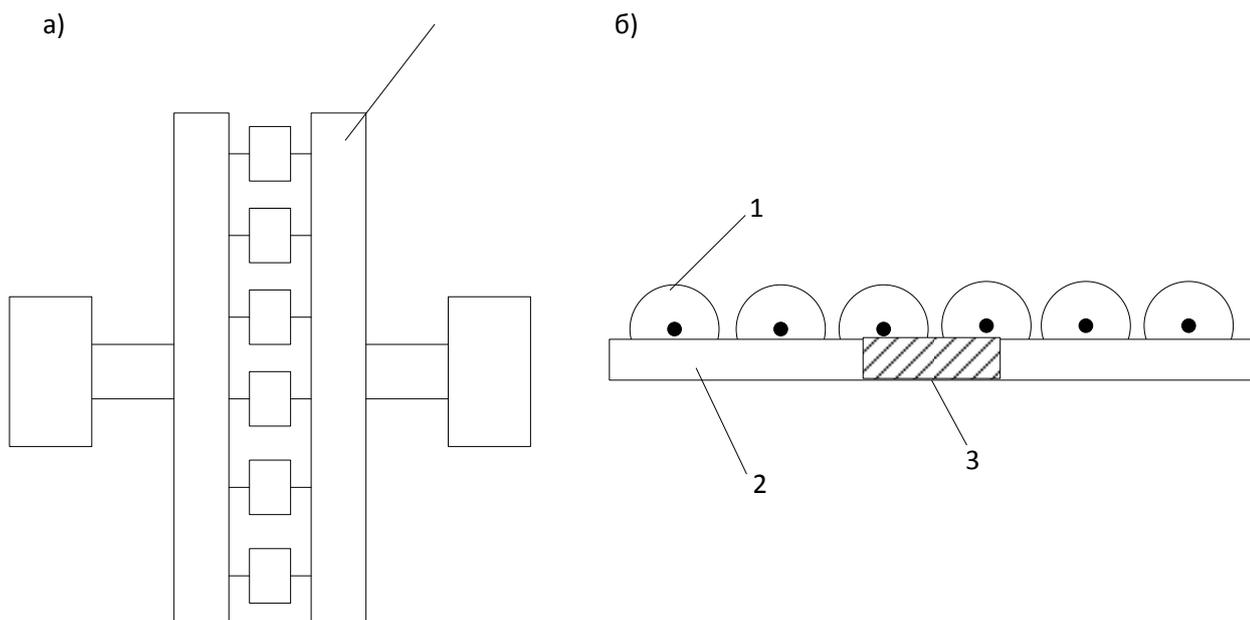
Устройство блокировки роликов: а – вид сверху; б – вид сбоку; 1 – ролики; 2-блокирующая колодка; 3 – привод
